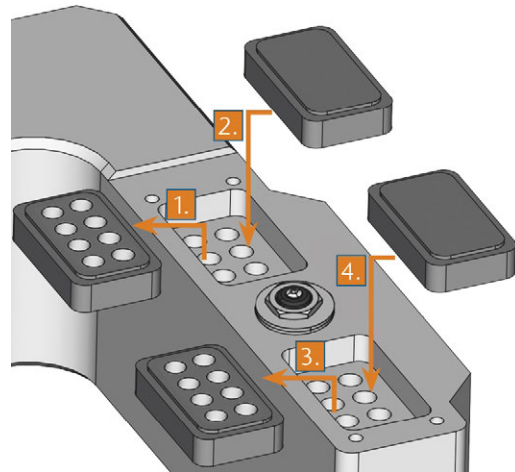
LOS NUEVOS INSERTOS DE ALMACÉN DE HERRAMIENTAS (DERECHA, SIN POSICIONES DE HERRAMIENTAS) SUSTITUYEN A LOS VIEJOS INSERTOS (IZQUIERDA, CON POSICIONES DE HERRAMIENTAS)
